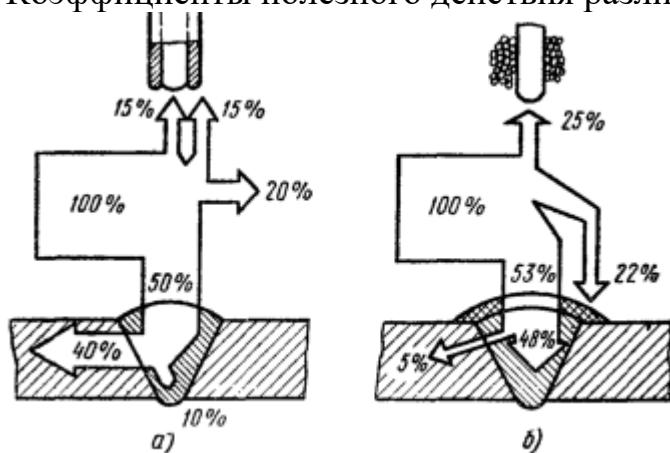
Тепловой баланс дуги при сварке:
